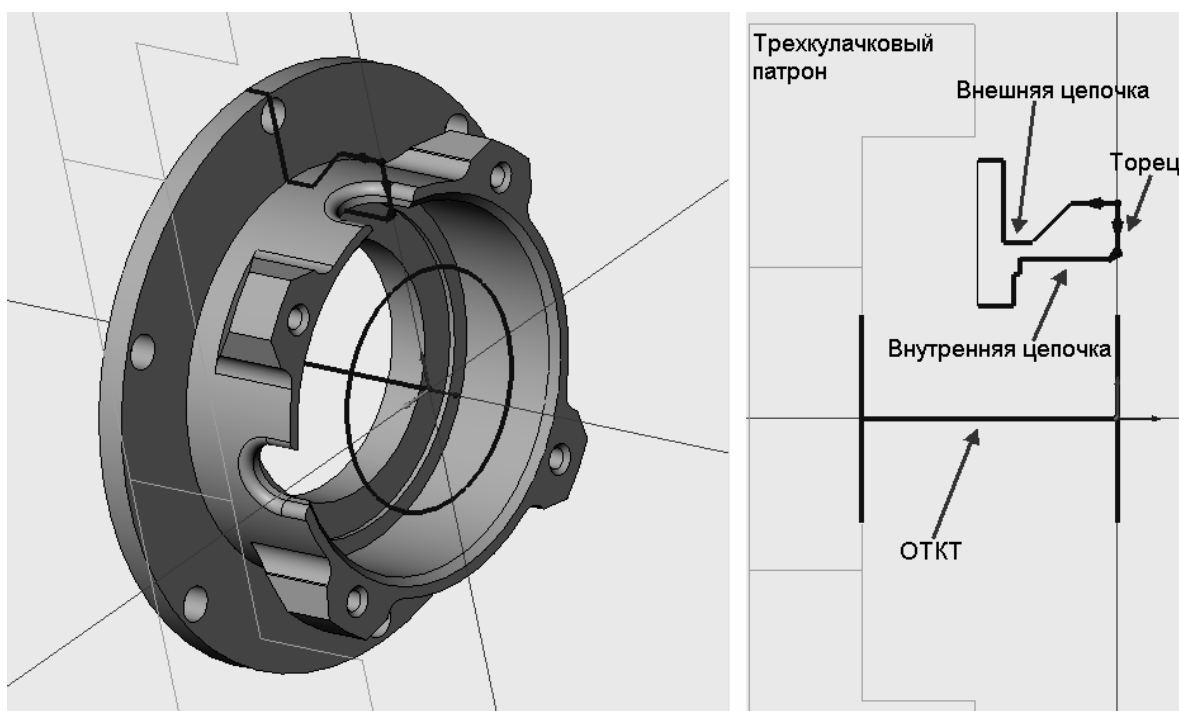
Расположение цепочек обработки на 3D-модели заготовки
